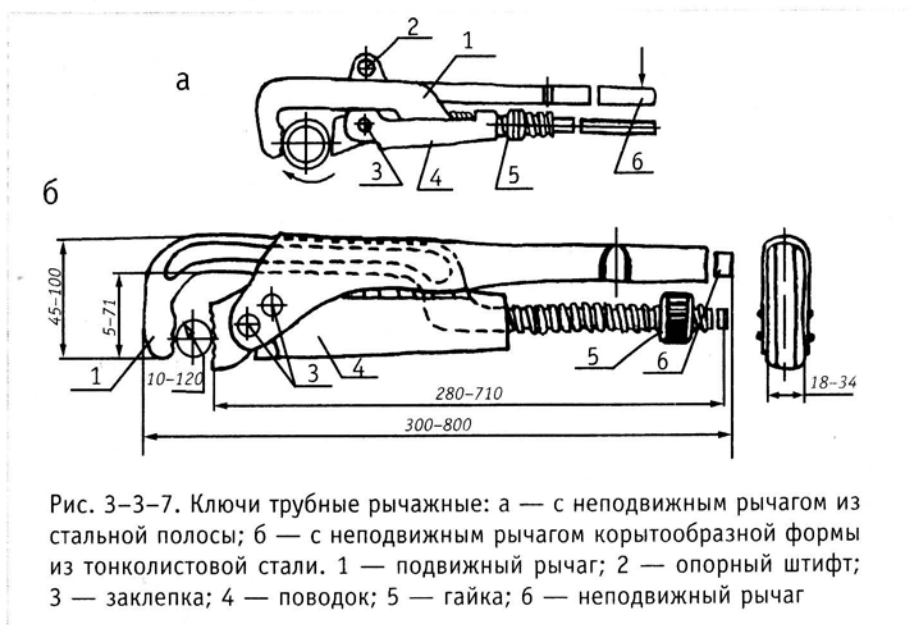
Ключи трубные рычажные: а — с неподвижным рычагом из стальной полосы; б — с неподвижным рычагом корытообразной формы из тонколистовой стали. 1 — подвижный рычаг; 2 — опорный штифт; 3 — заклепка; 4 — поводок; 5 — гайка; 6 — неподвижный рычаг
